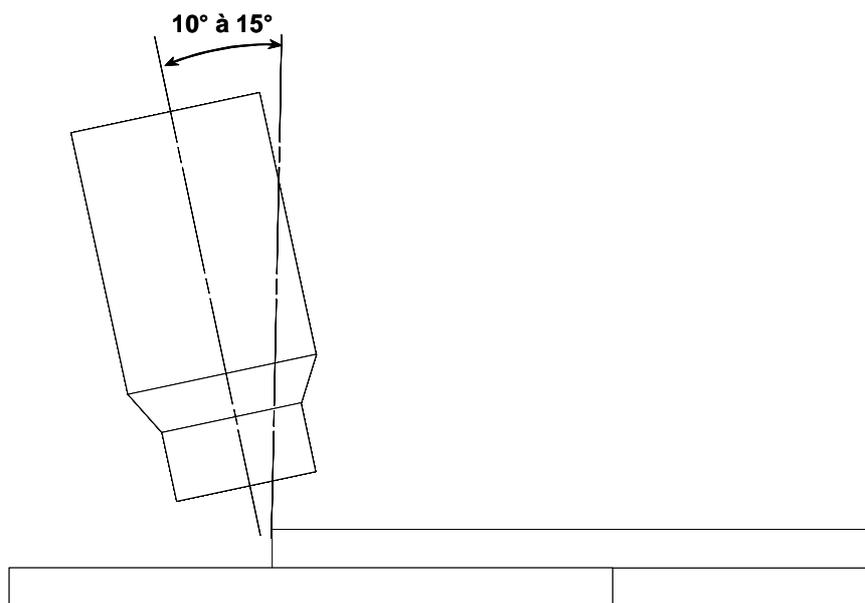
Figure B : Profil décrivant les angles pour un assemblage à recouvrement
